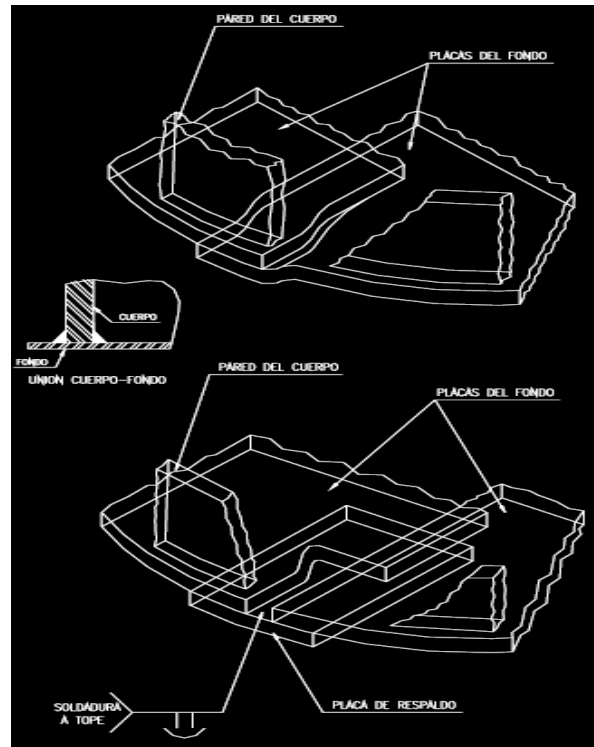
Preparación del material a soldar entre cuerpo-fondo
